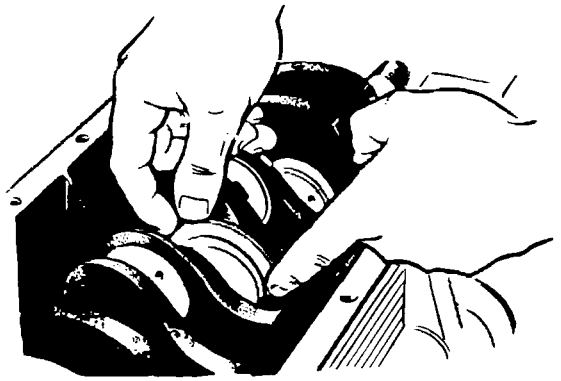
Установка упорных полуколец в гнезда картера среднего коренного подшипника
